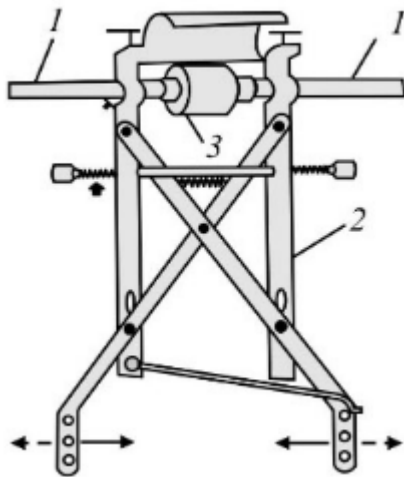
Термитная сварка многопроволочных проводов:
